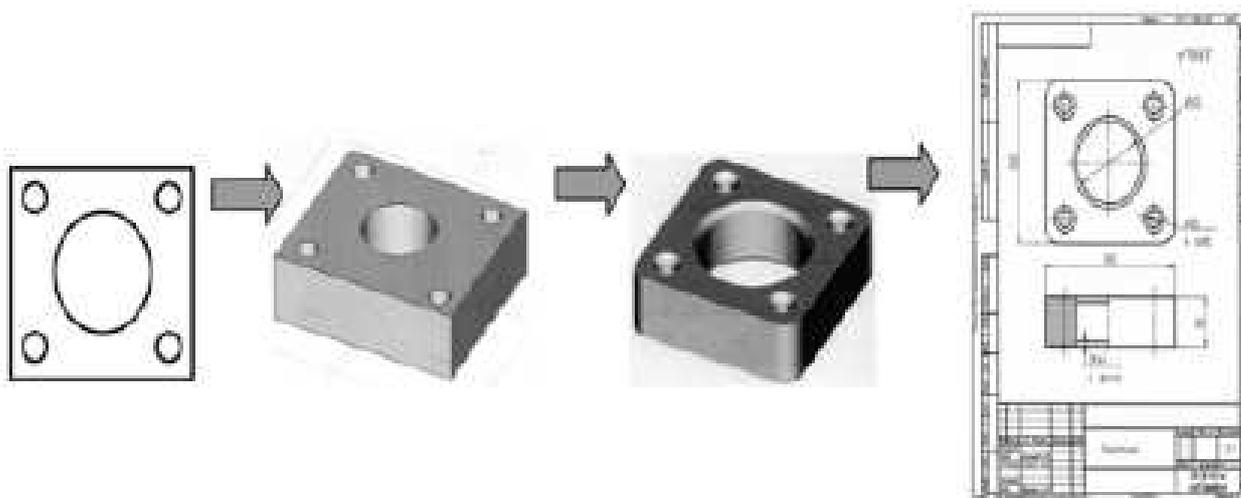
Схема компьютерного инжиниринга при разработке чертежа
